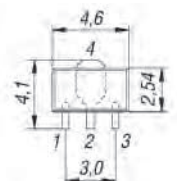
Pinbelegung und Abmessungen (SOT-89)
